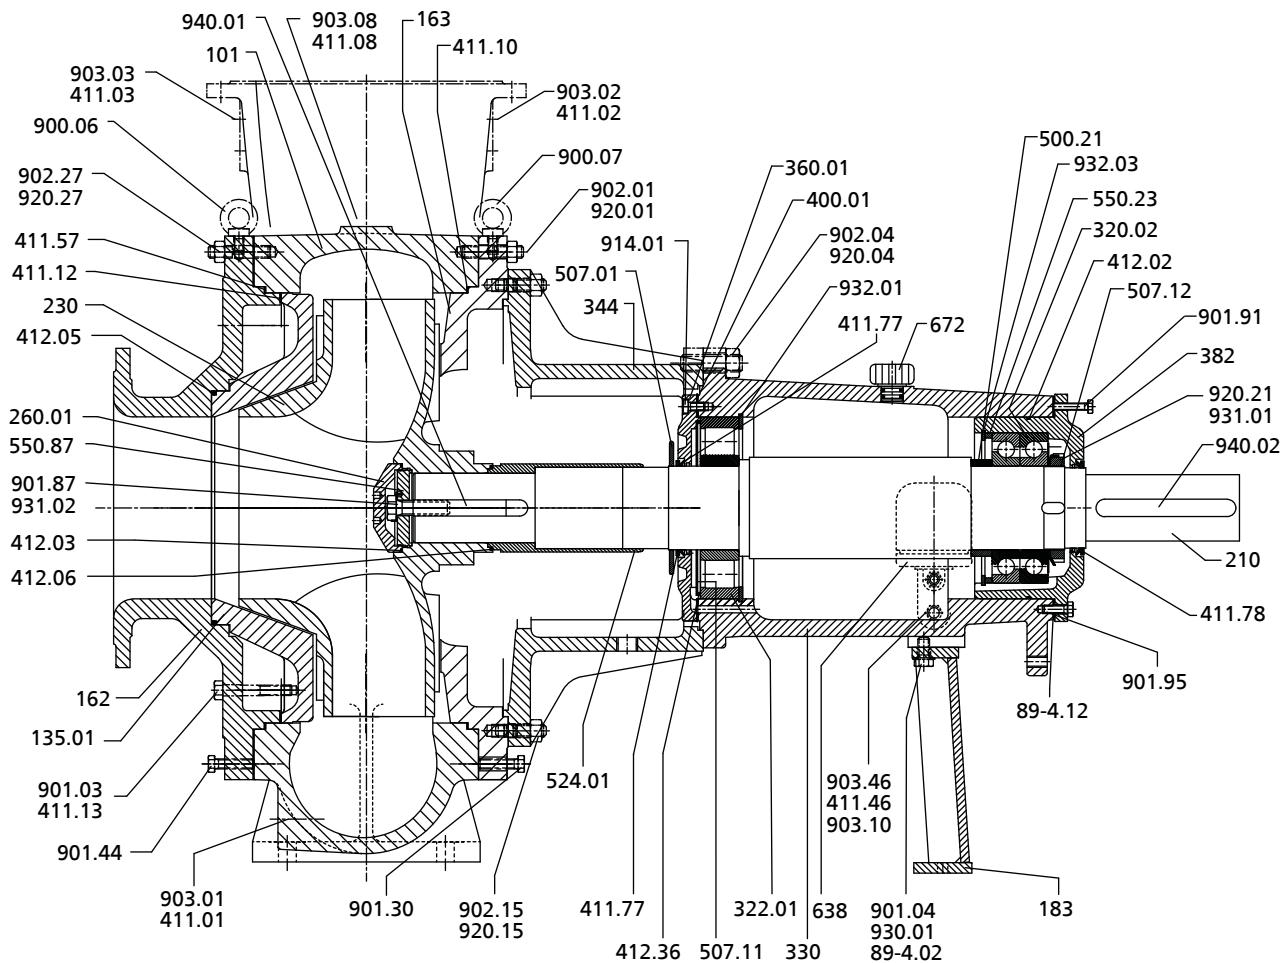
Gesamtzeichnung Pumpe mit Lagerträger P10ax bis P12sx (Baugröße 500-400-0710, 500-400-0713)
